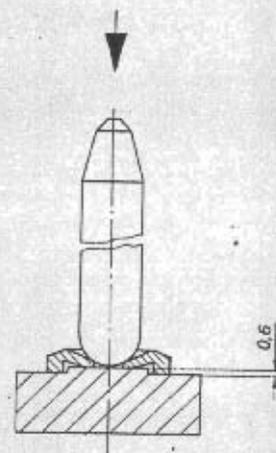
Zurückschlagen des Düsenchutzplättchens mit einer passenden Schlagvorrichtung
